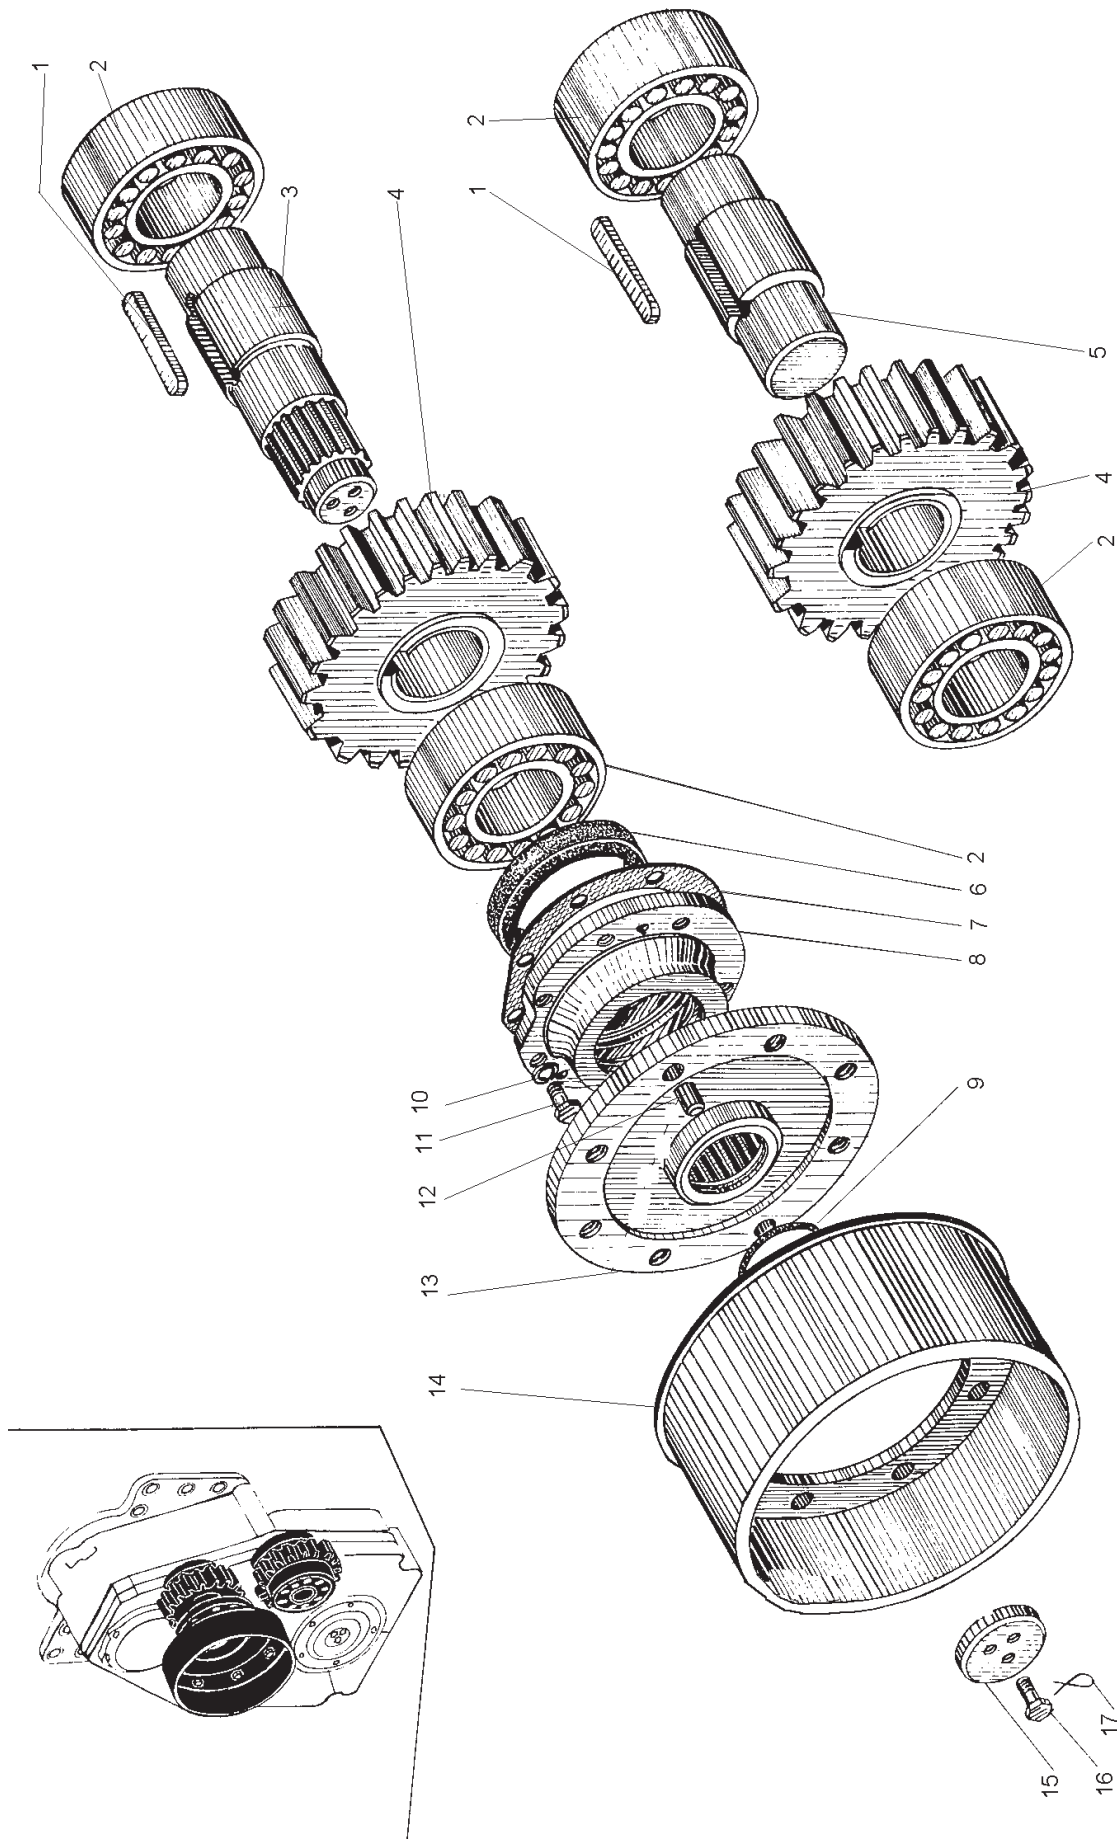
Редуктор раздаточный (ДЗ-98.10.05.000-02)
